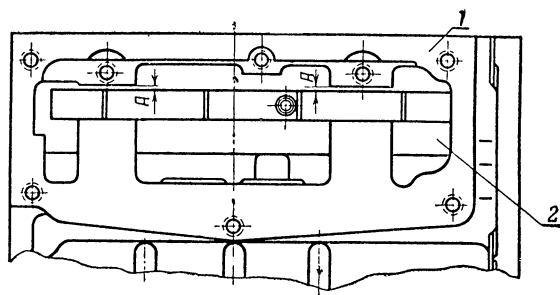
Зазор между рейкой и направляющими корпуса насоса:
